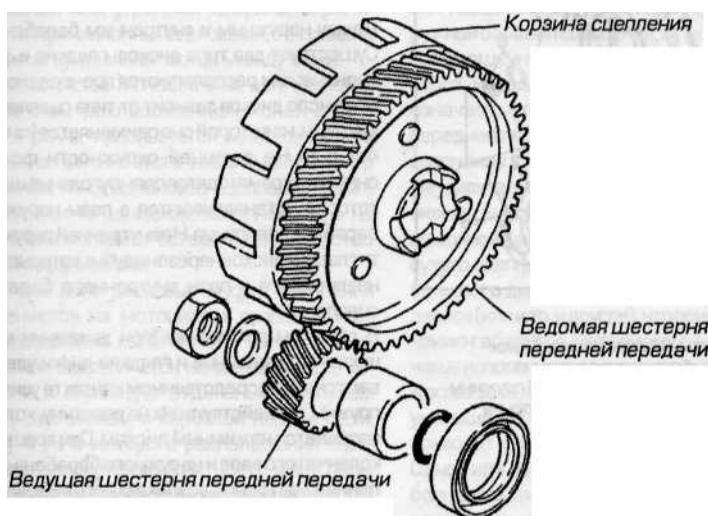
Устройство косозубой зубчатой передней передачи
